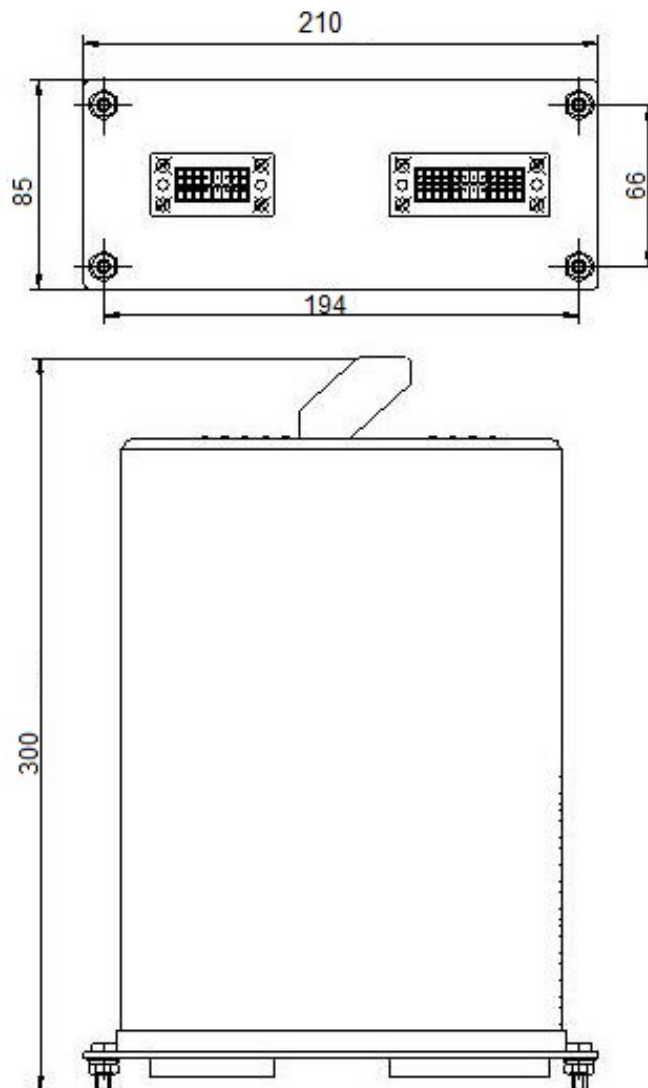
Габаритно-установочные размеры ПДК
